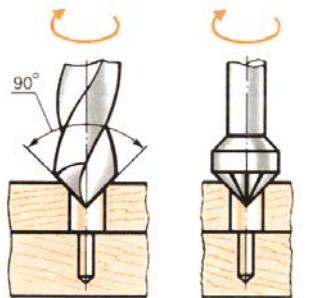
Подготовка гнезда под головку шурупа сверлом
